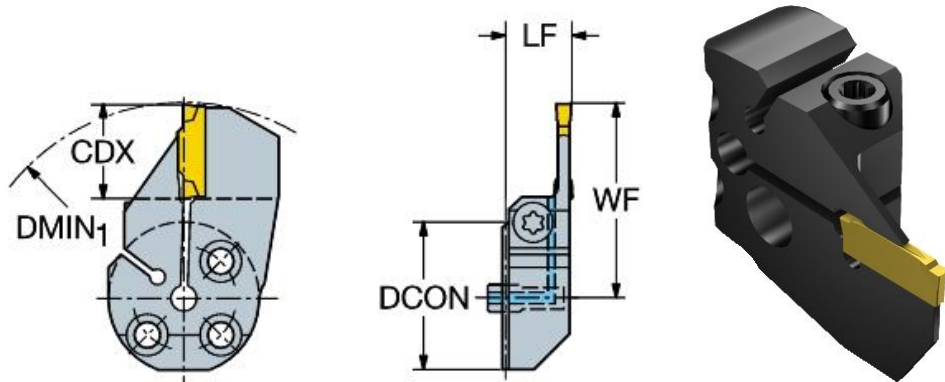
Зовнішній вигляд Різцевої головки 570-40R123K18B
